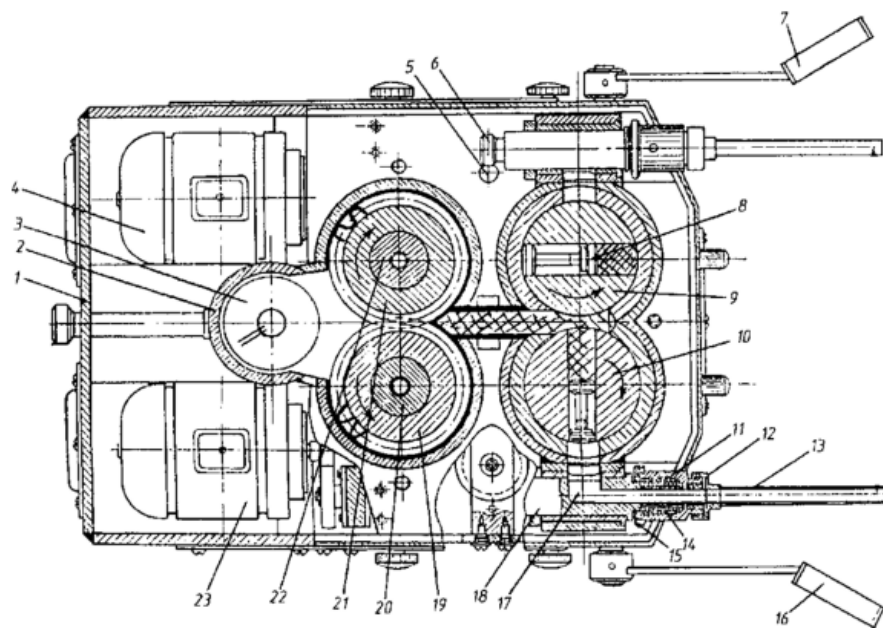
Розріз робочого механізму шприца П-ФШТ «Донбас»: 1 – станина машини; 2 – корпус; 3 - шнек, що подає; 4, 23 - двигуни перекручувача; 5 – рейка; 6 – зубчасте колесо; 7, 16 – педалі; 8 – поршень дозатора; 9, 10 – диски дозаторів; 11 – втулка; 12 – накидна гайка; 13 - цівка; 14 – підшипники; 15 - зубчасте колесо; 17 - радіальний отвір; 18 - вал перекручувача; 19 - шестерня витіснявача; 20, 22 - вали; 21 - зубчасте колесо
